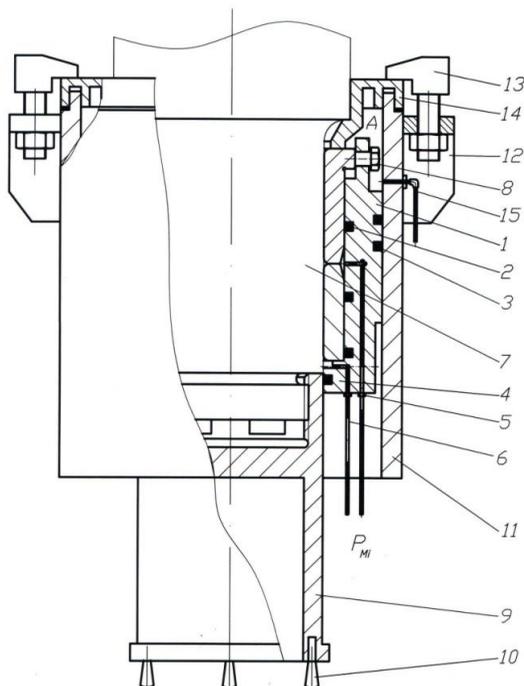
Принципиальная схема устройства для распрессовки колец буксовых подшипников колёсных пар
